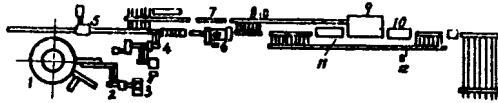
匈牙利切佩尔钢管厂的顶管机组平面布置图
